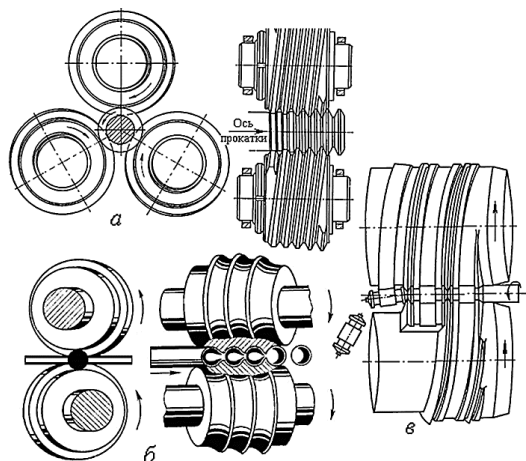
Схемы поперечно-винтовой прокатки: *а* — винтовой поверхности; *б* — шаров; *в* — коротких валиков
